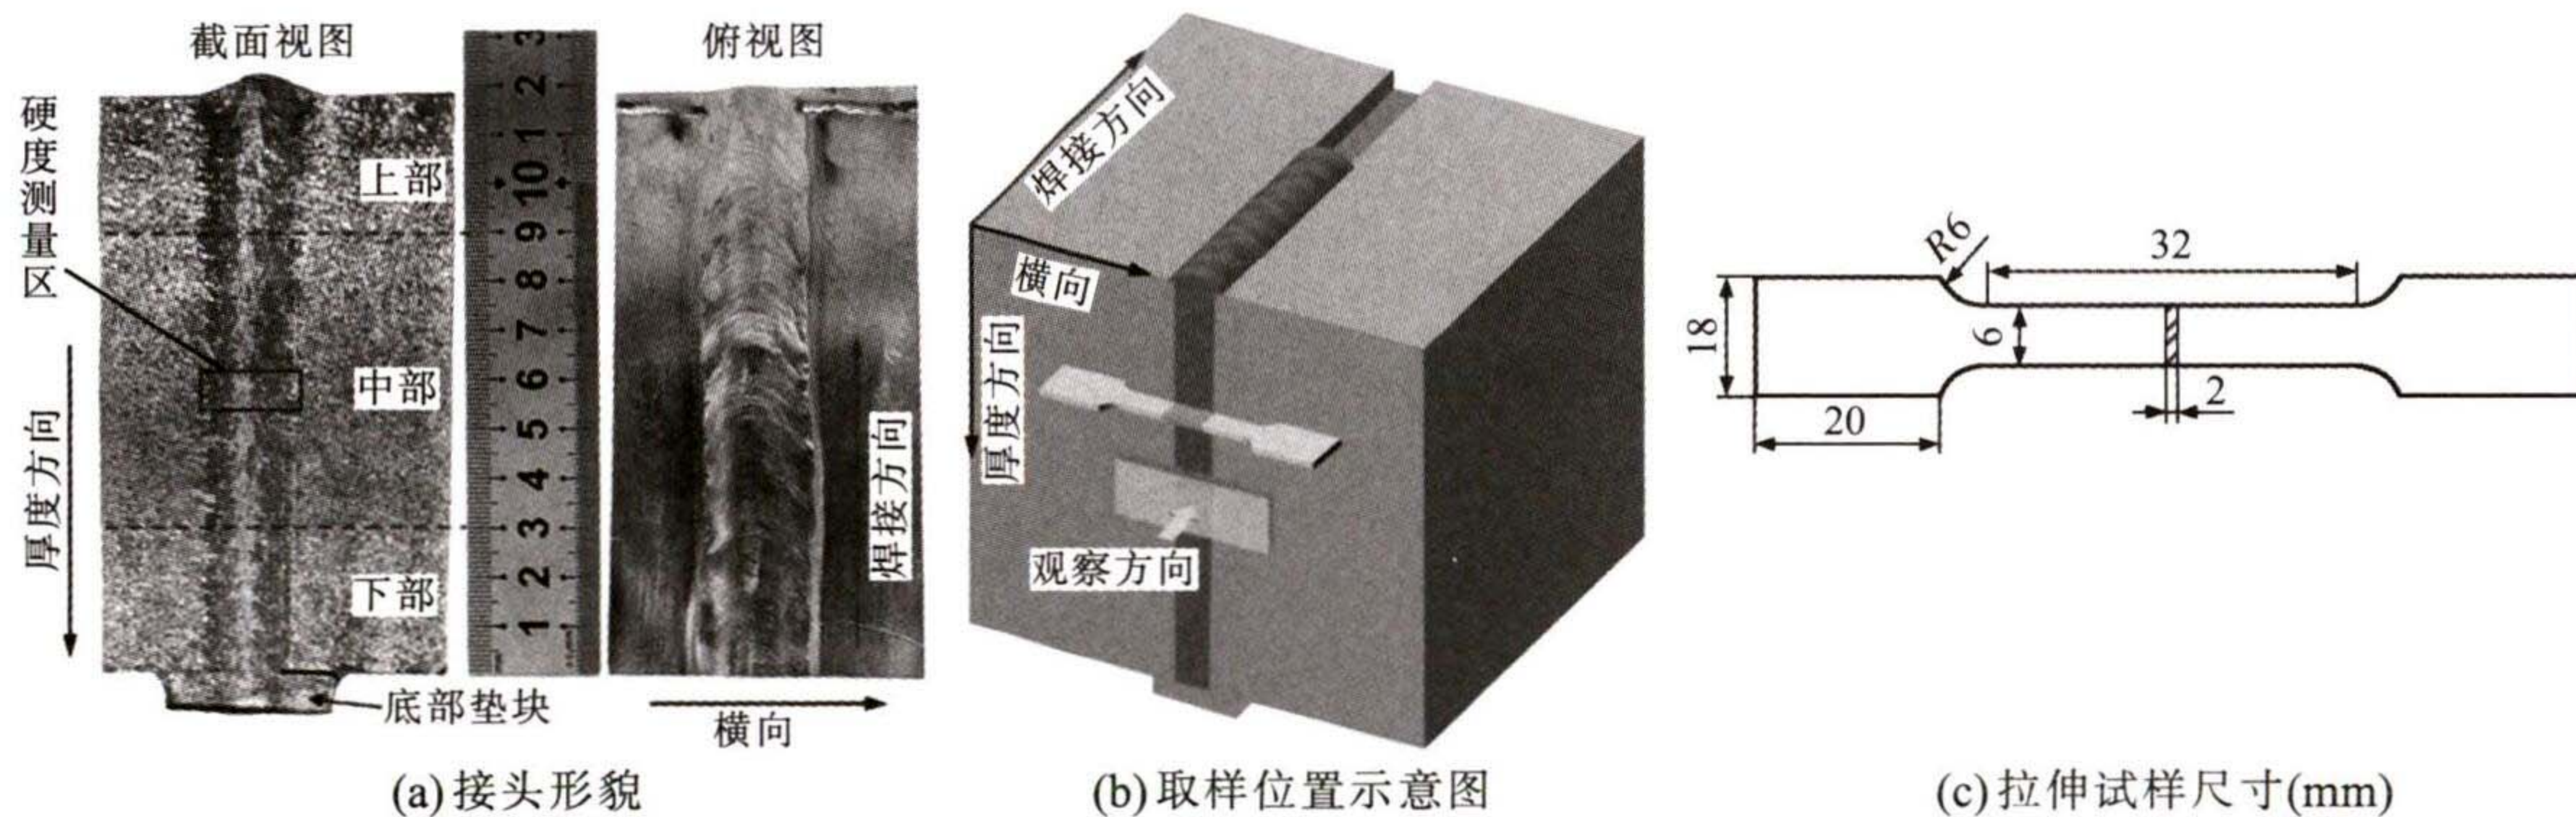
TA17 合金磁控窄间隙 TIG 焊接头及取样位置图
